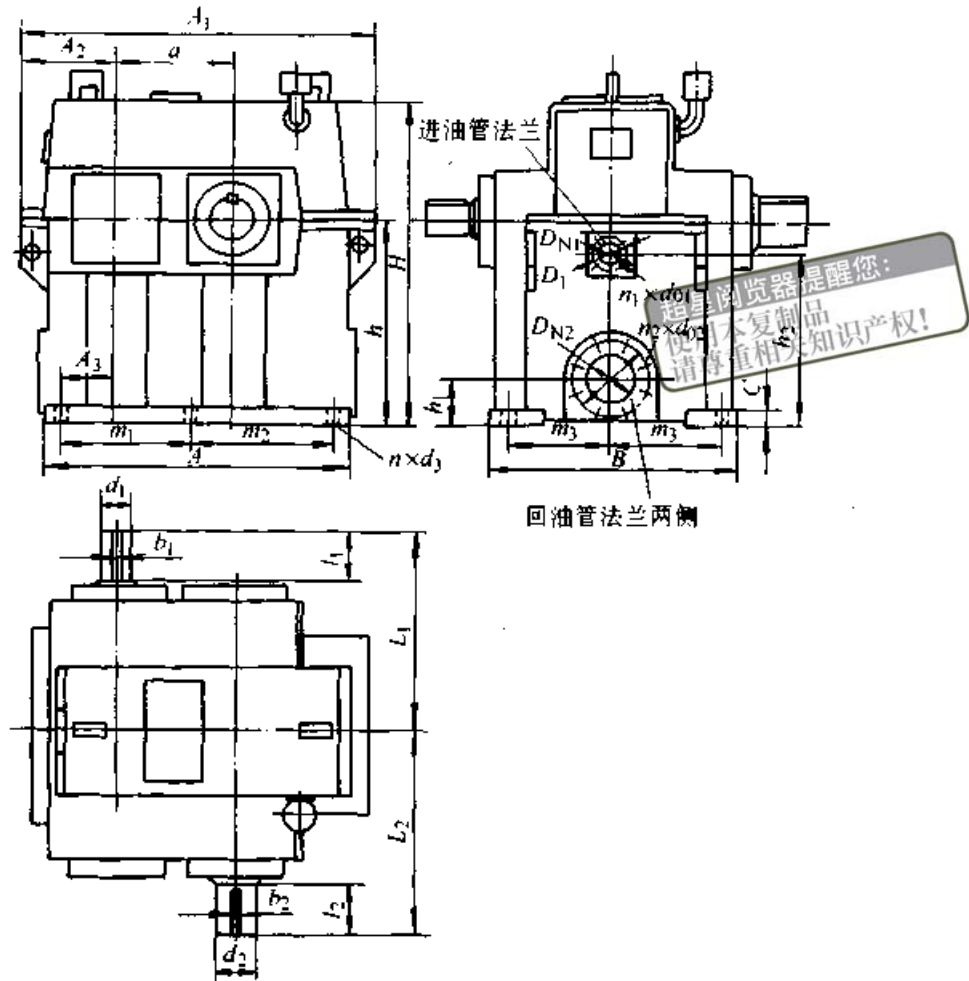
GS450~GS670 齿轮箱结构尺寸
